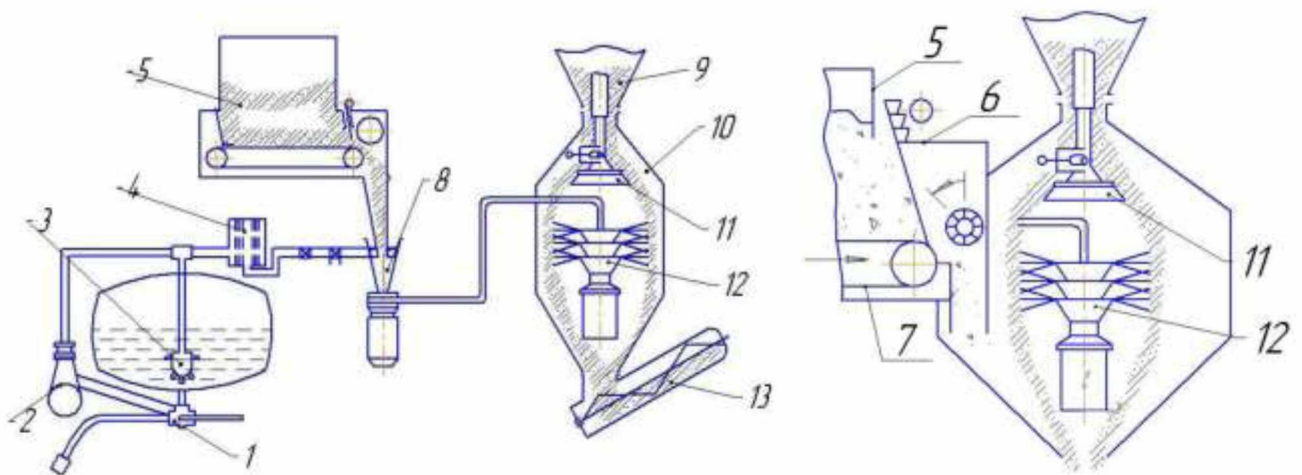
Штанговий протруювач: 1 – ресивер; 2 – компресор; 3 – водомасловідділяч; 4 – зворотний клапан; 5 – дозатор-живильник отрутохімікатів; 6 – запірний клапан; 7 – шаблон-накладка; 8 – штанга; 9 – наконечник
